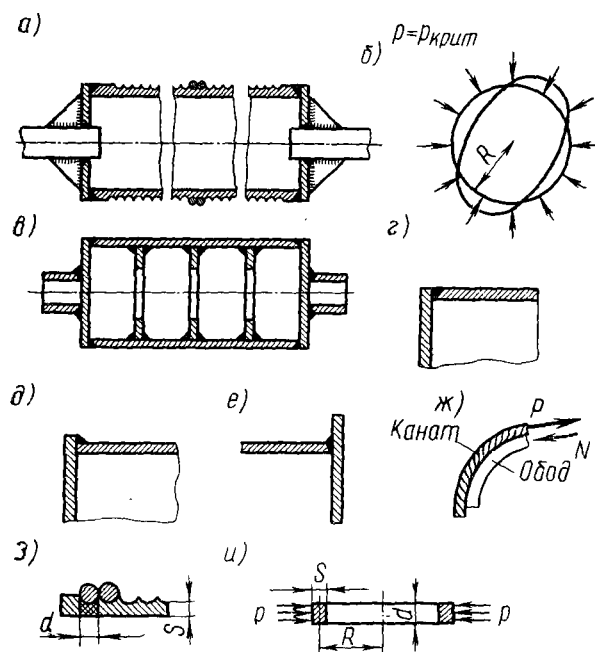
К расчету сварных барабанов; а) общий вид; б) при потере устойчивости в) усиленные кольцевыми ребрами жесткости; г, д, е) соединения цилиндрической части с торцевой стенкой; ж) к определению усилий в барабане от натяжения троса; з) к определению рабочей толщины стенки; и) устойчивость кольца от P
